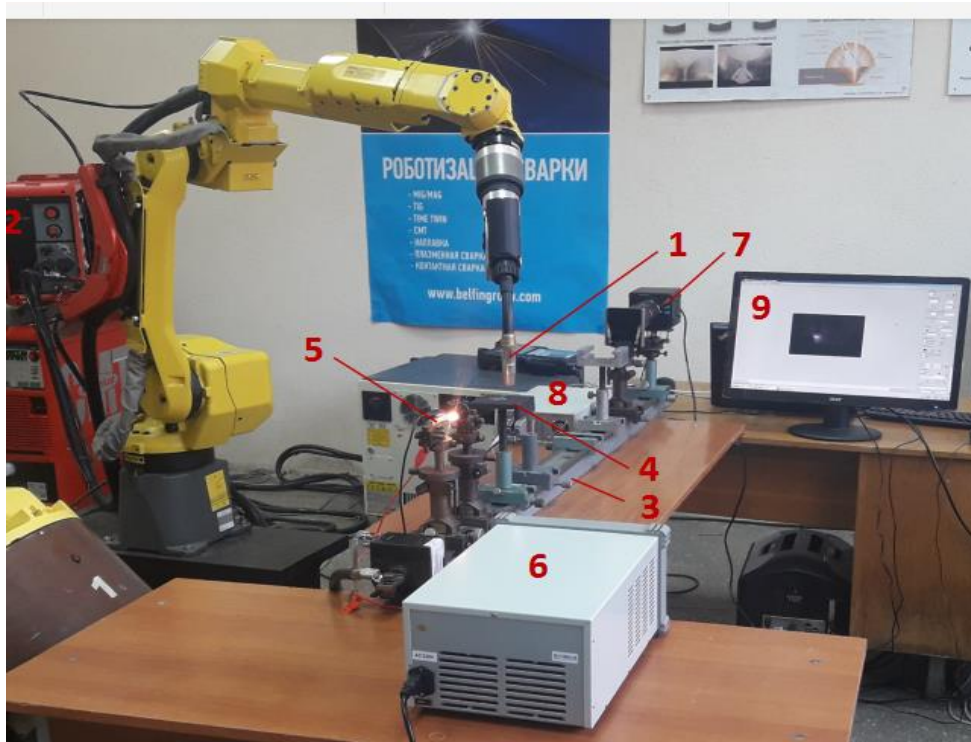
Внешний вид информационно-измерительного комплекса: 1- сварочная горелка в составе робототехнического комплекса; 2- сварочный источник питания; 3- оптическая скамья; 4- сварочный стол; 5- источник светового излучения с фокусирующей линзой; 6- блок питания источника света; 7- камера высокоскоростной съемки с набором фильтров; 8- регистратор параметров сварочных процессов с датчиками; 9 - персональный компьютер с разработанным программным обеспечением
